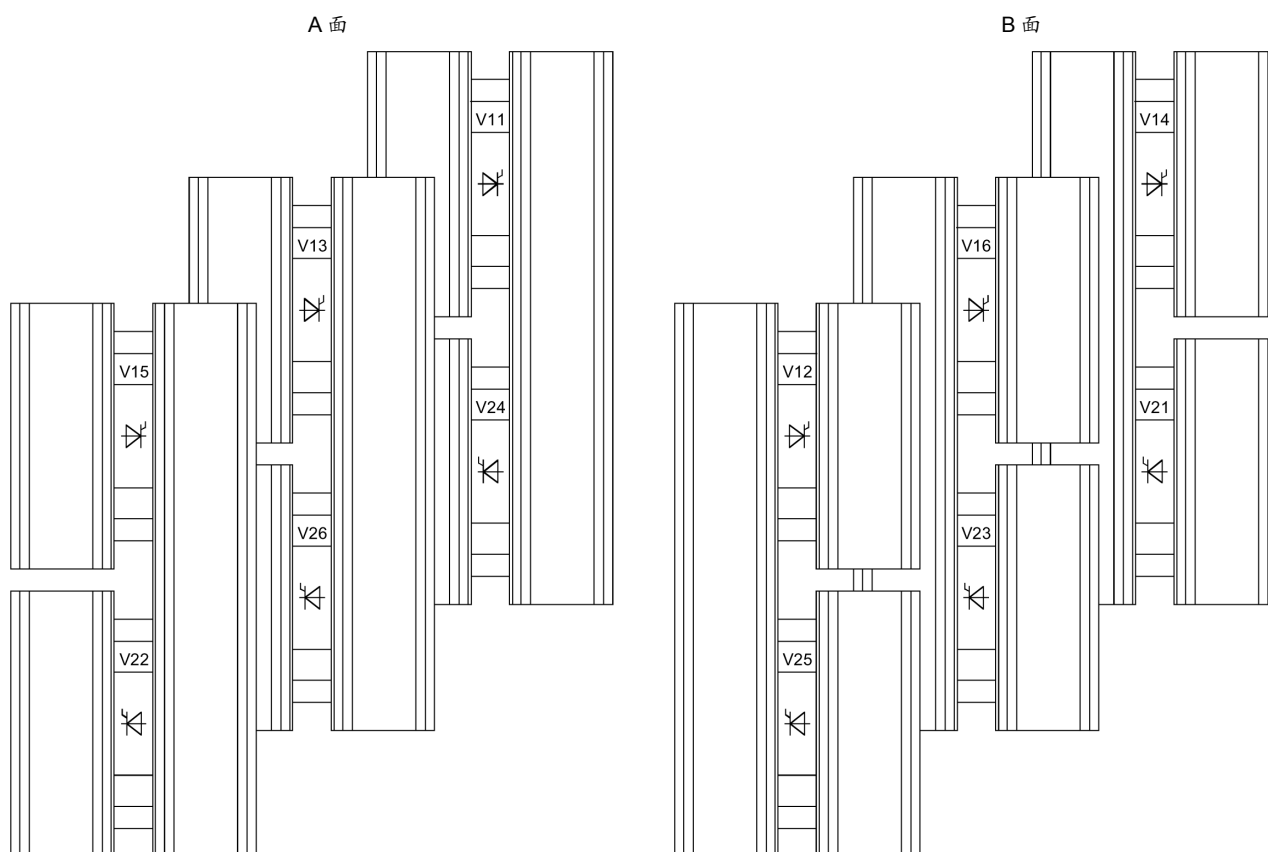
晶闸管组件的布置，装置右侧视图，规格 K (亦见 2.4 节中外形尺寸图)
